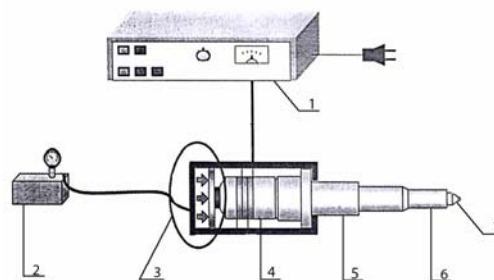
Схема установки для ультразвуковой упрочняющей обработки с пьезокерамическим преобразователем: 1 – ультразвуковой генератор; 2 – воздушный компрессор для обеспечения статической нагрузки на инструмент; 3 – механизм регулировки усилия, обеспечиваемого пневмосистемой; 4 – пьезокерамический источник; 5 – бустер; 6 – волновод; 7 – сферический наконечник
